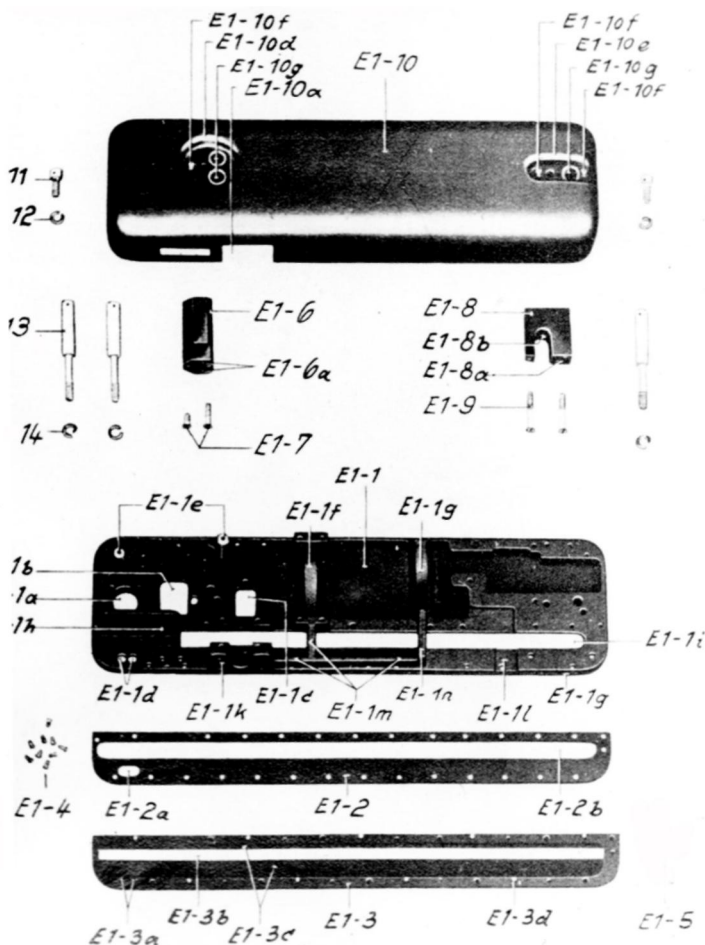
ED 151 B; Gehäuse, Einzelteile
